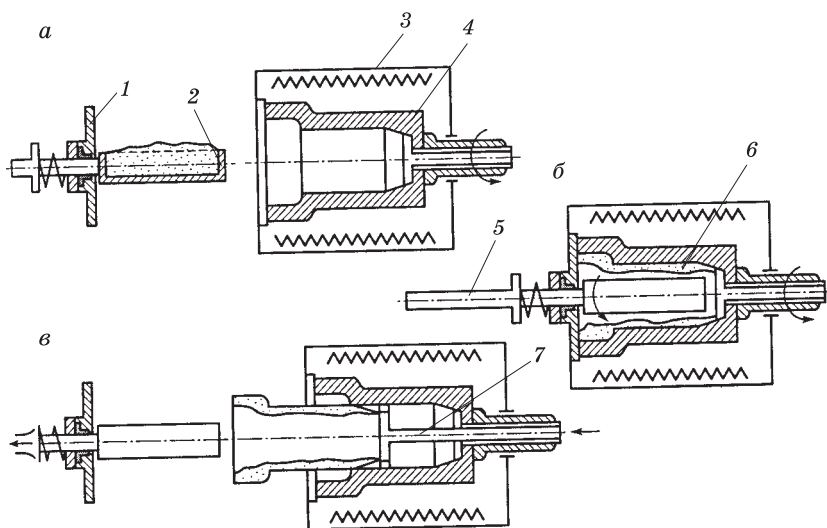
Схема центробежного изготовления оболочкового стержня: а — поджим ящика к бункеру; б — надув смеси в ящик; в — сбор избытка смеси
